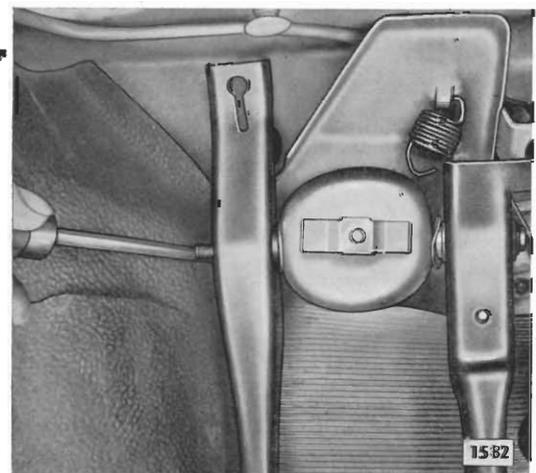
Pedalwelle mit Schraubenzieher herausdrücken
